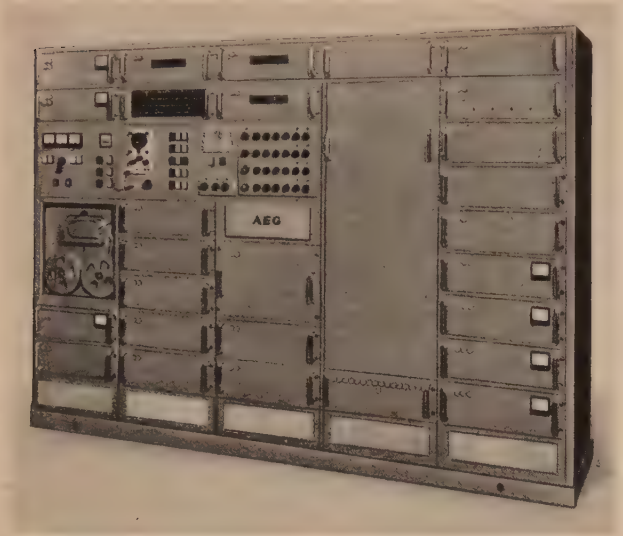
Steuerschrank für die numerische Werkzeugmaschinensteuerung
